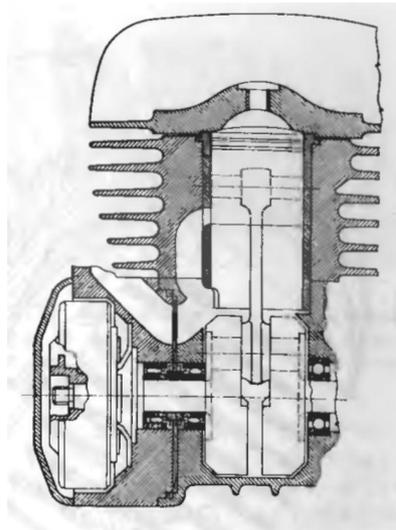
Пример установки золотника непосредственно на коленчатом валу двигателя
